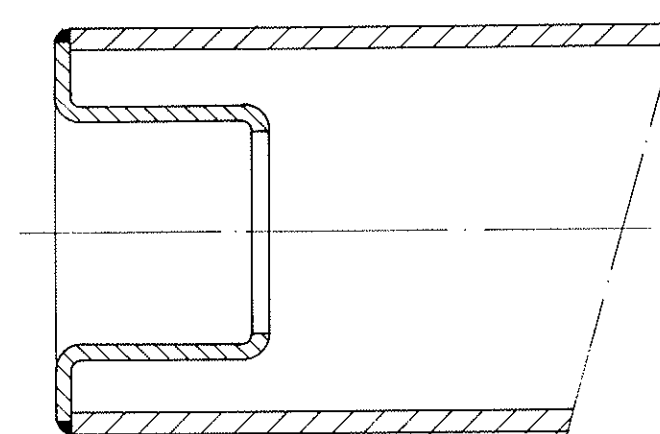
Soldadura exterior hasta \varnothing 108 mm.
